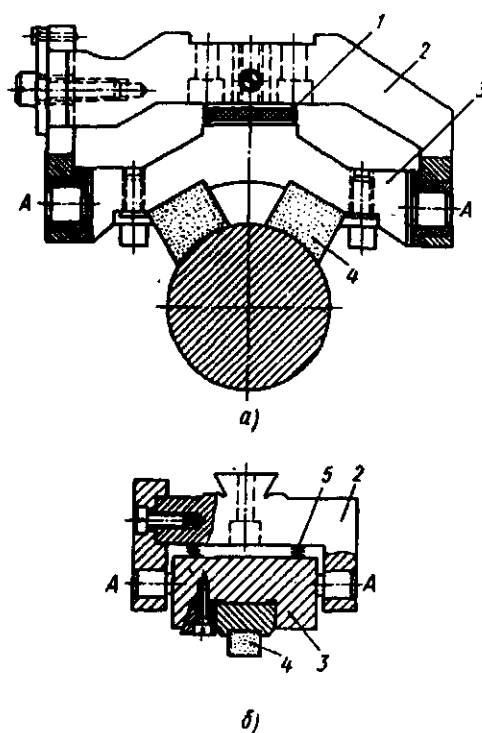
Державка с брусками для суперфиниширования цилиндрической (а) и плоской (б) поверхностей: 1 – гайка; 2 – рамка; 3 – корпус державки; 4 – брусок; 5 – пружины
